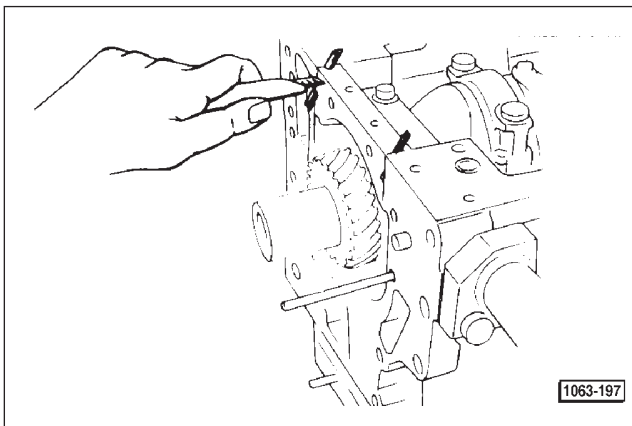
Couper la partie des joints en caoutchouc dépassant le bord du bloc-moteur de sorte à les aligner à ce dernier. Cela doit se faire soit sur le côté avant que sur celui arrière.
